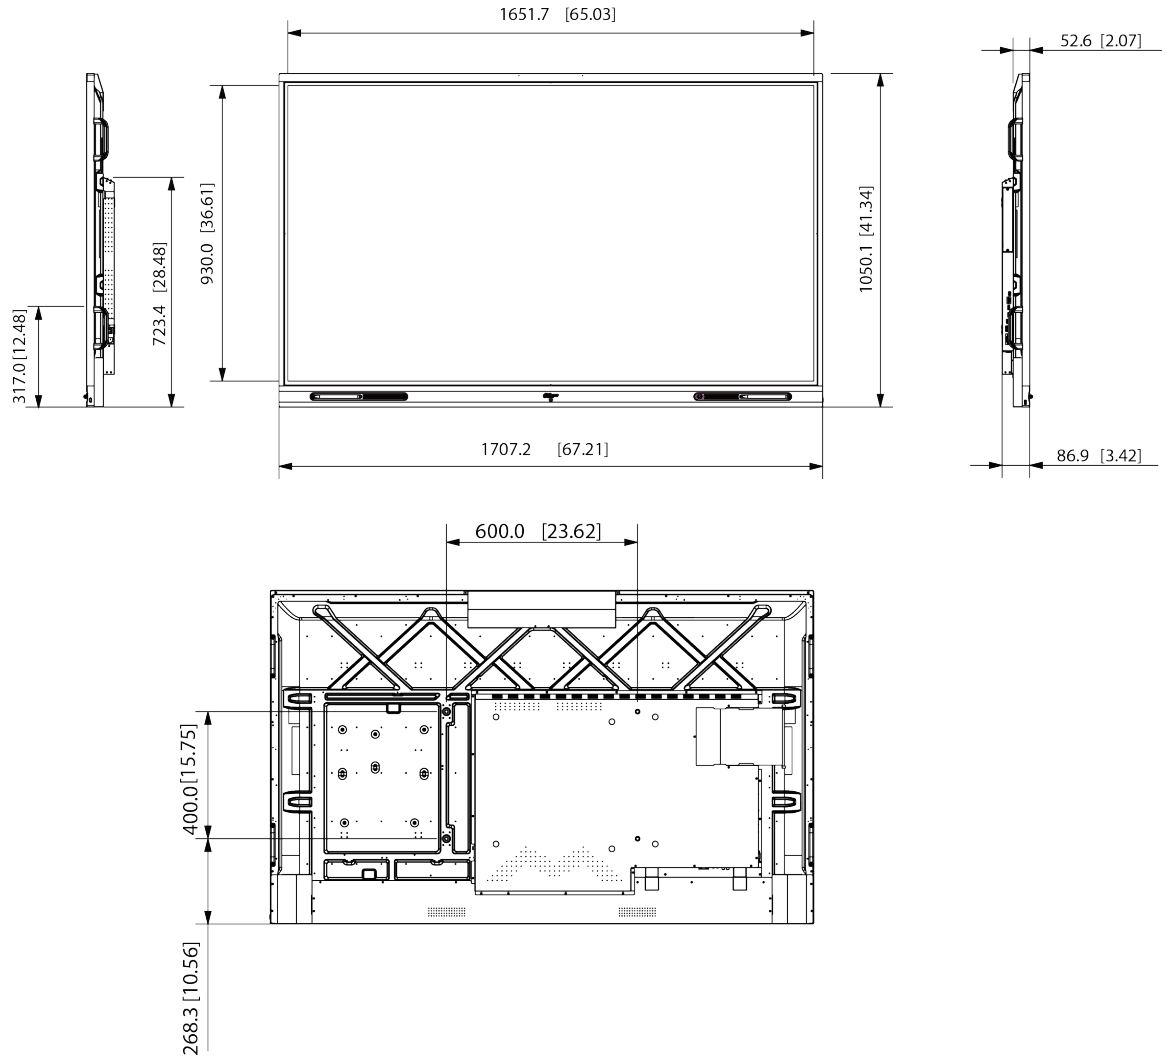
Dimensions (sans caméra) (mm [pouces])
